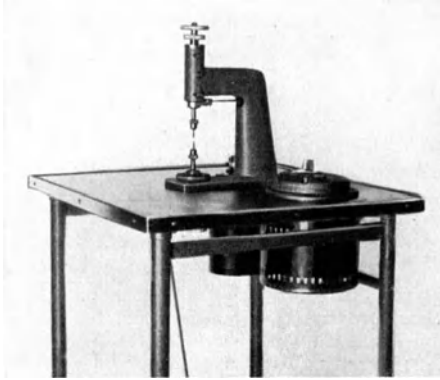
Punktschweißmaschine mit Feinregulierung und Stromauslöser (Schweißbegrenzer) für kleine Elektroden-teile; Stoßleistung 1 bis 2 kVA (Lieferwerk: Gladitz, Berlin).
